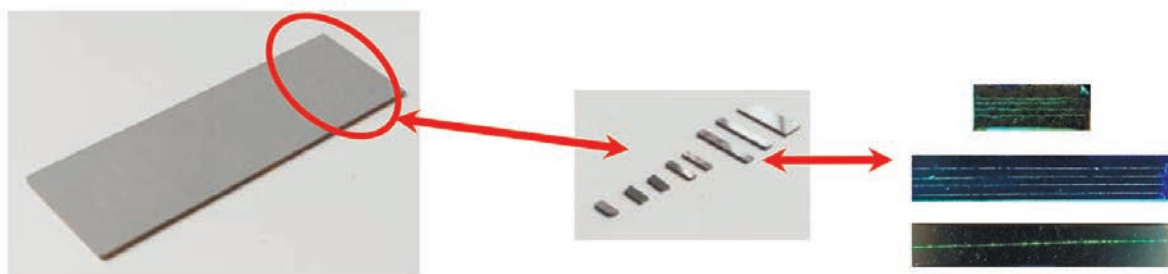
Вид изготовленных образцов для оценки качества нанесения и результаты их капиллярного экспертного контроля.
